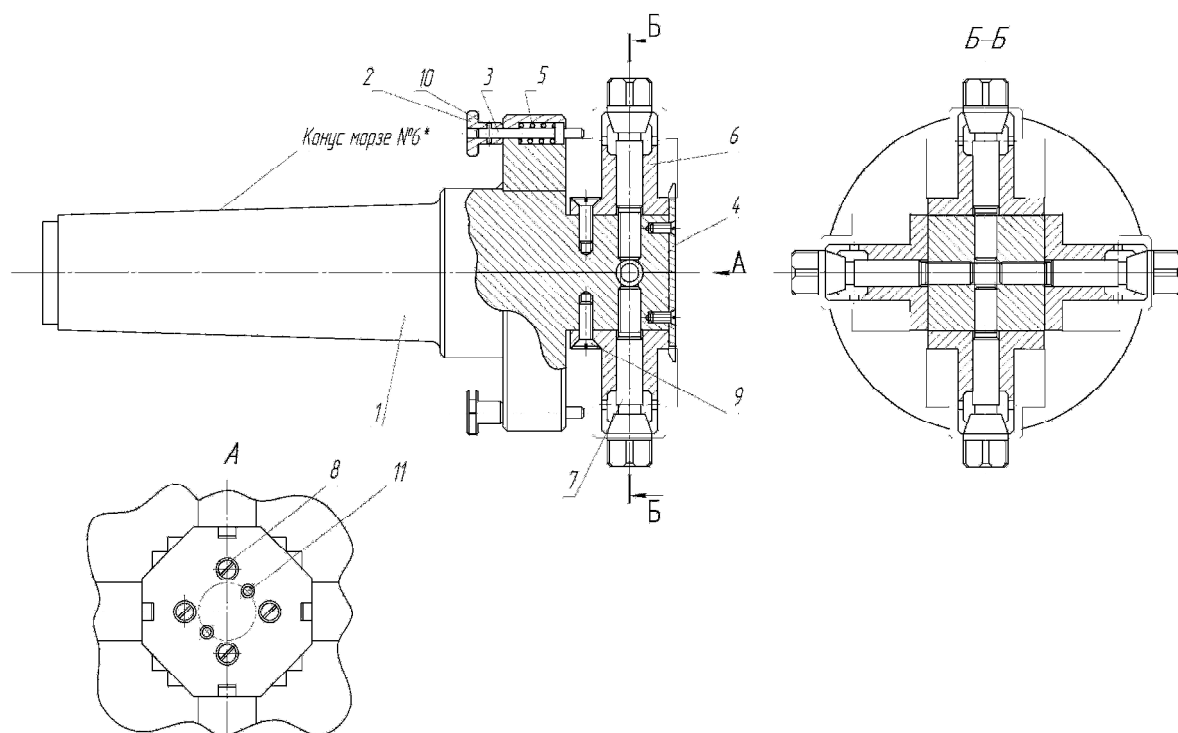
Приспособление ПТ-1468-11-690 ГОСНИТИ
